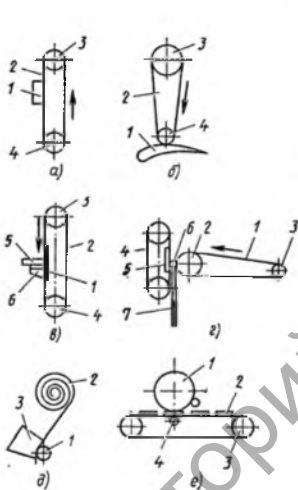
Основные схемы обработки шлифовальной лентой
